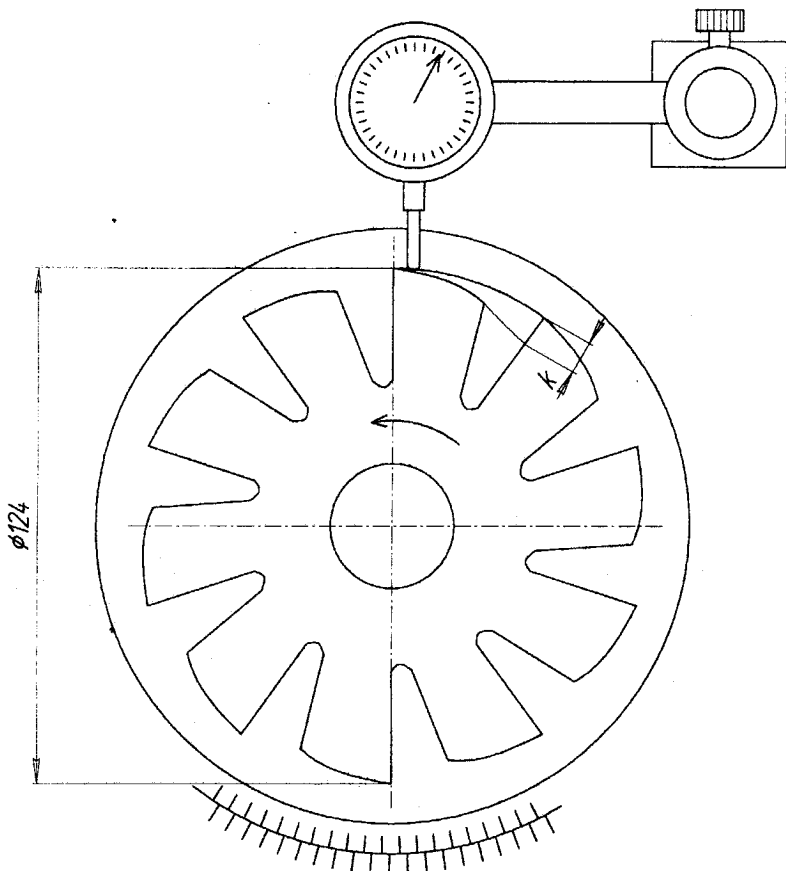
Схема вимірювання величини спаду затилку на задній поверхні зуба.
